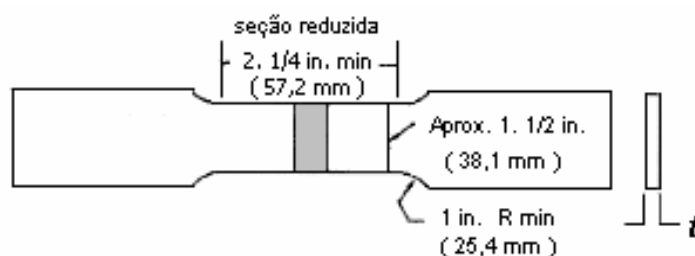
Corpo-de-prova para o ensaio de tração transversal de solda
